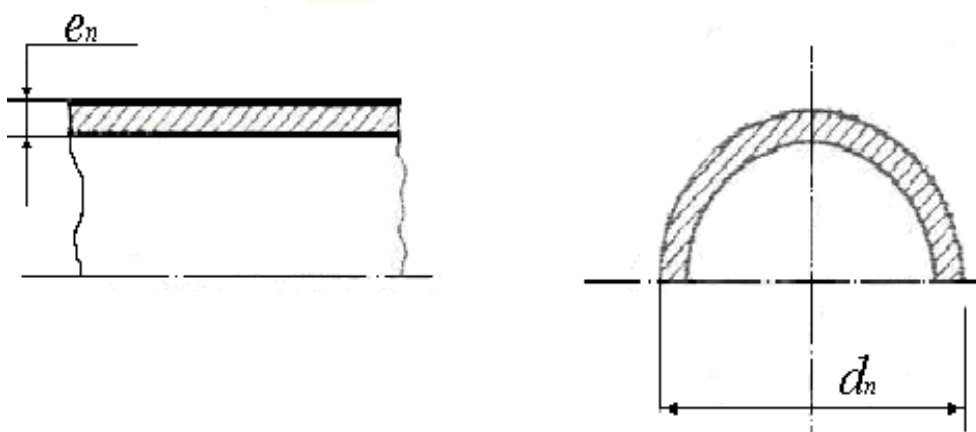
Продольный и поперечное сечение труб (без раструба) и гладкой части труб раструбных
